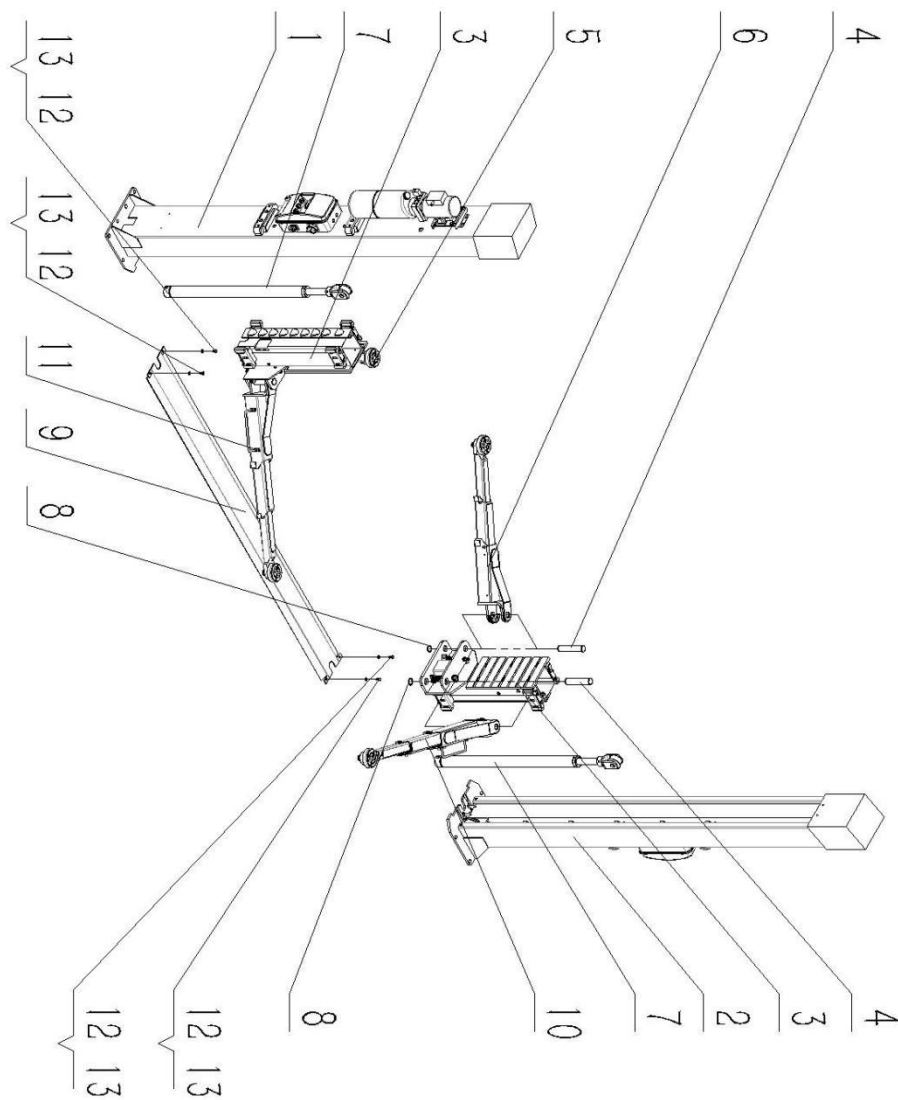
Gesamtansicht in Einzelteilen der Hebebühne
